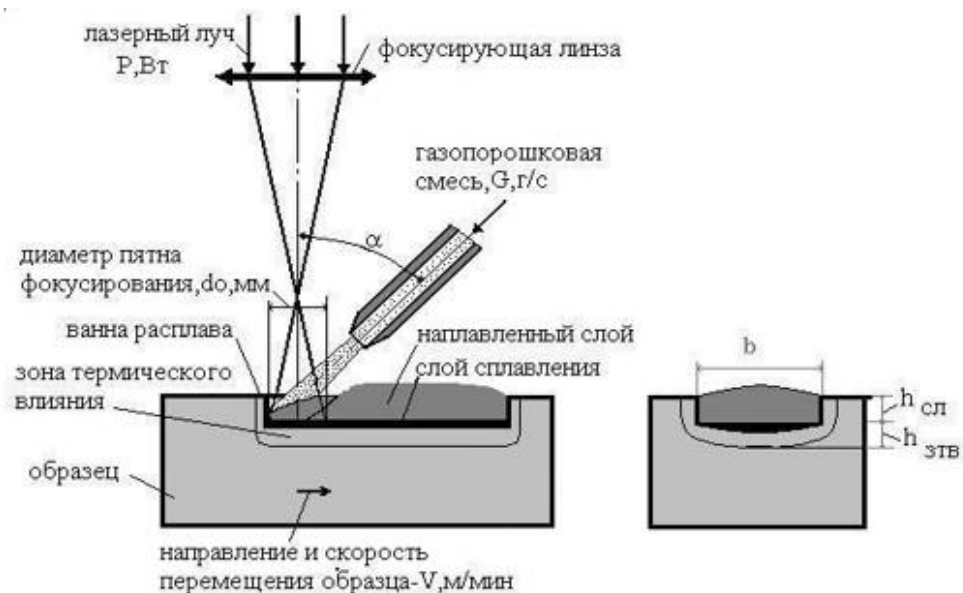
Схема лазерного газопорошкового наплавлення
